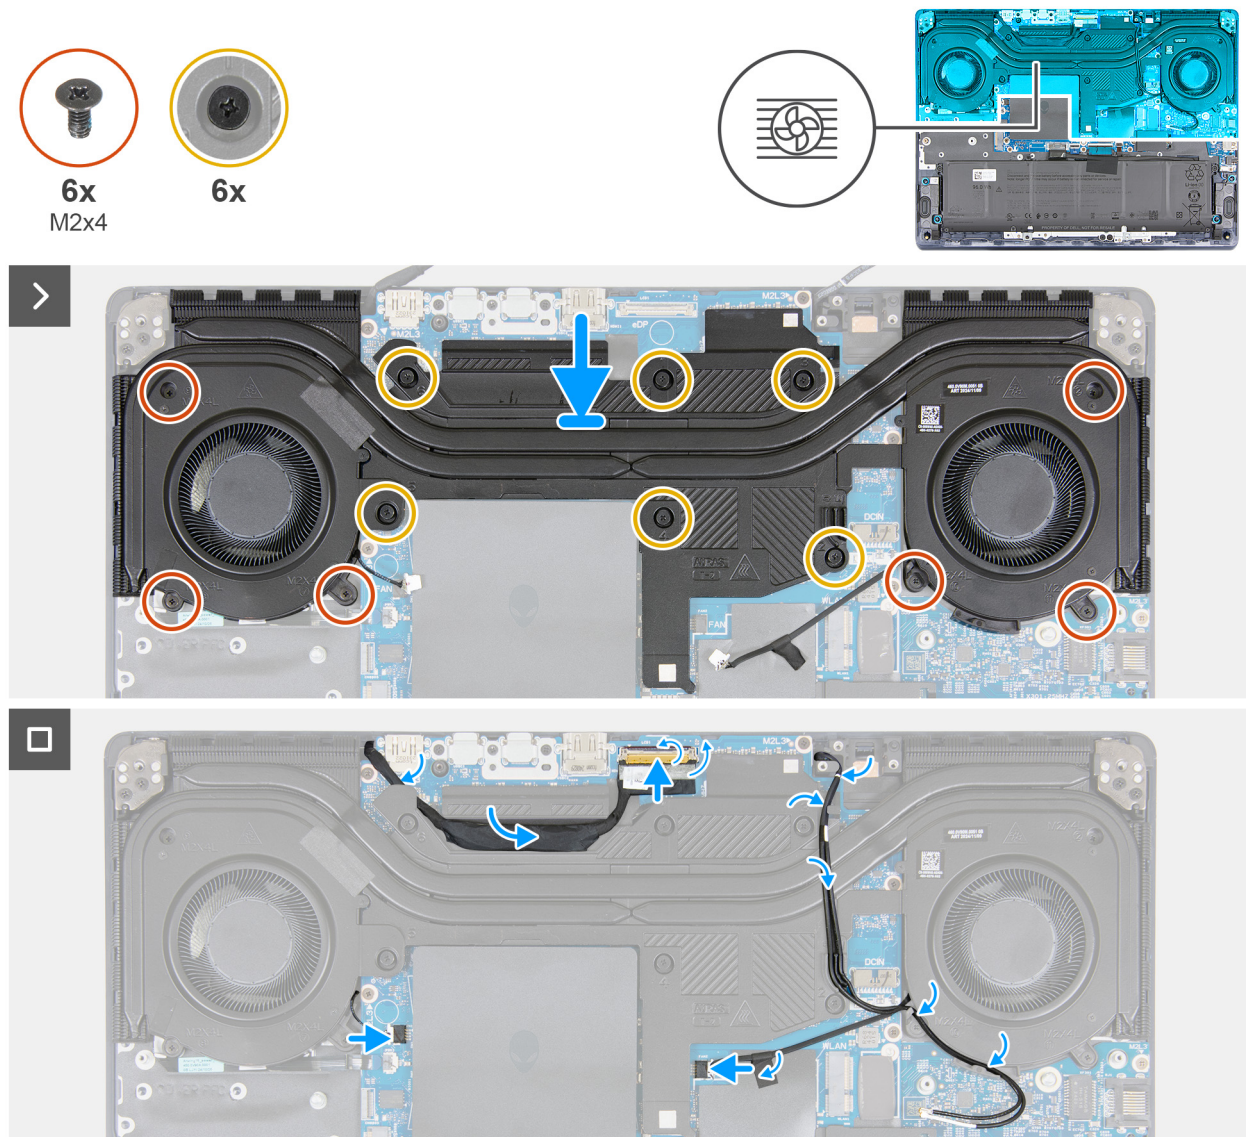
Como instalar o conjunto do ventilador e dissipador de calor
